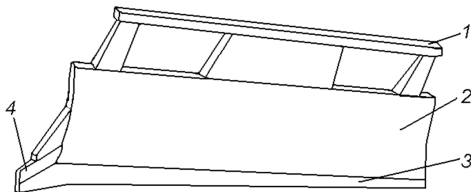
Однокорпусный кусторезный отвал: 1 – защитная конструкция; 2 – отвальная поверхность; 3 –режущая кромка; 4 – колун.
